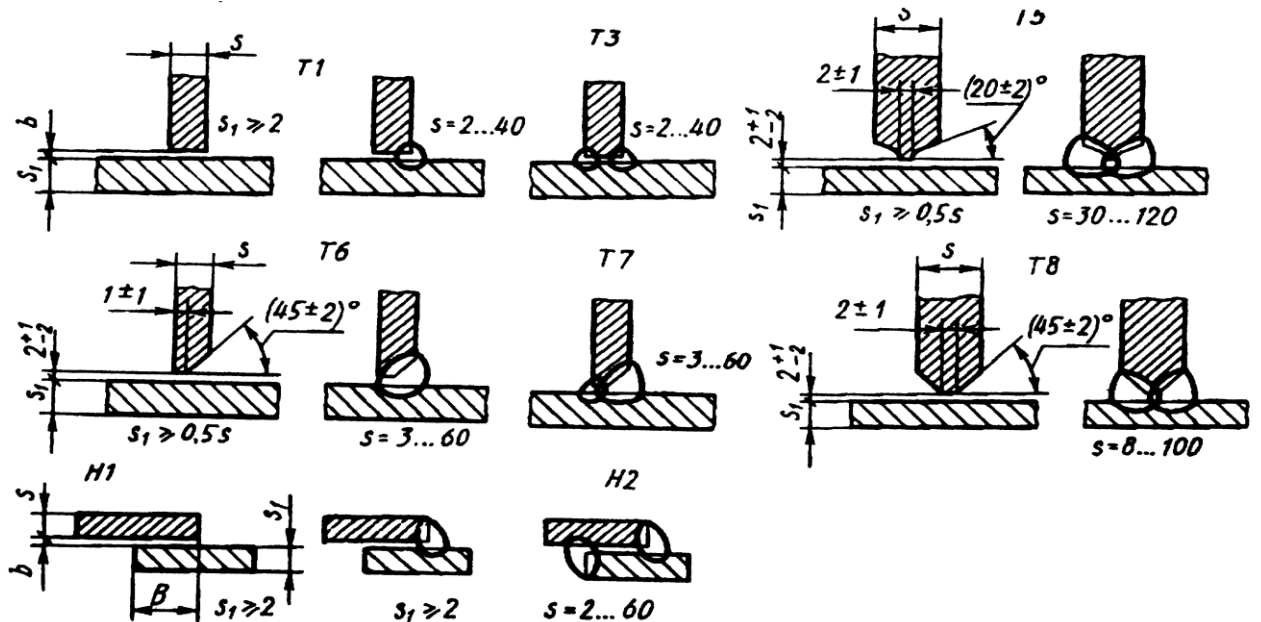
Форма поперечного сечения подготовленных кромок с размерами и сварного шва, а также стандартные условные обозначения тавровых - T1...T8 и нахлесточных - H1, H2 сварных соединений.
